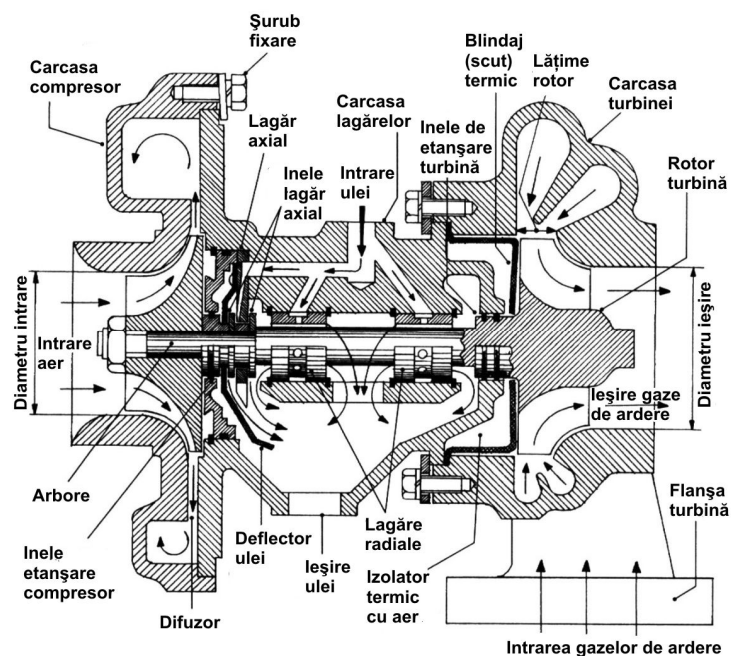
Secțiune prin ansamblul compresor – turbină
